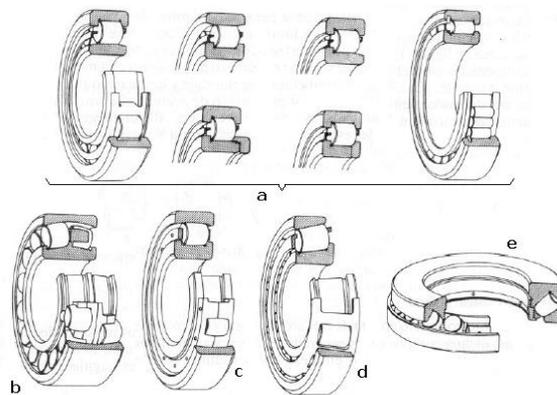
Rodamientos de rodillos. (a) de una sola hilera bajo diversas formas constructivas (b) de dos hileras oscilante (c) oscilante de una hilera (d) cónico (e) axial oscilante.
